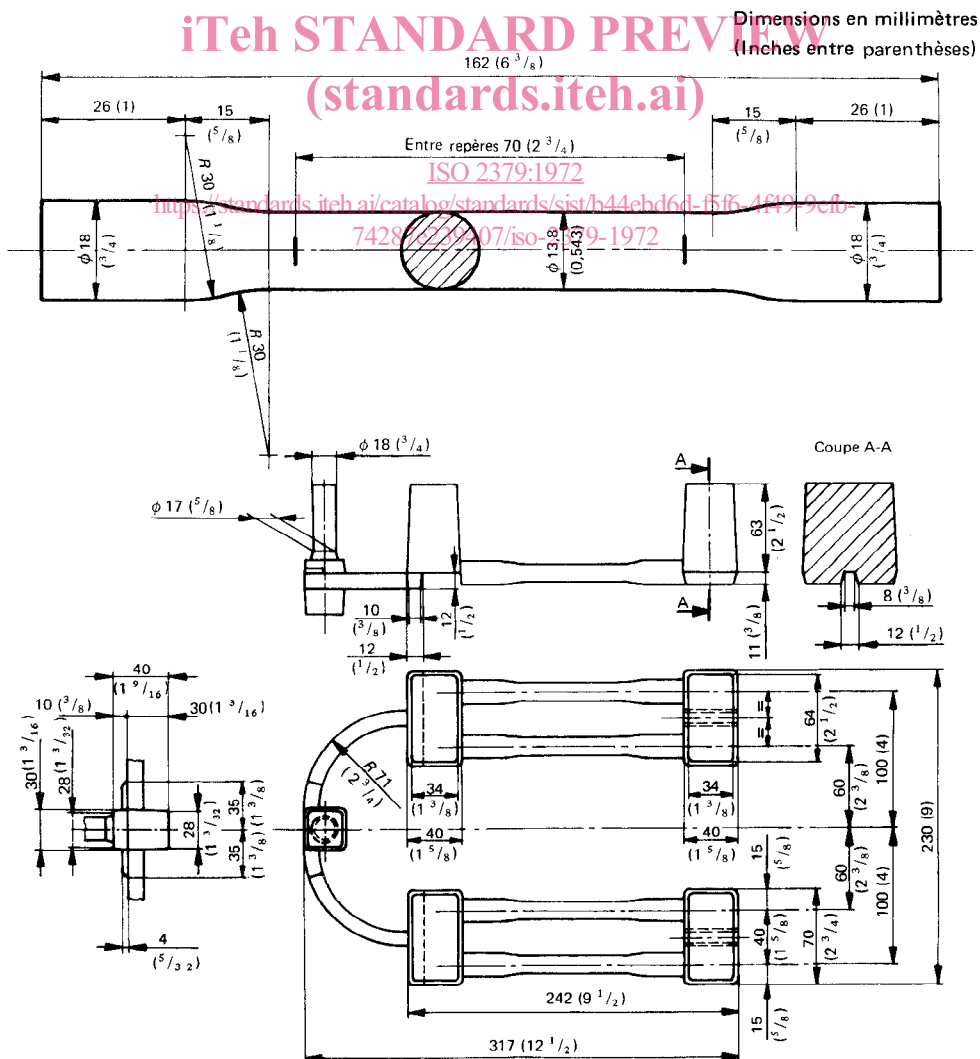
FIGURE — Éprouvette de référence et modèle de moule pour jeu de quatre éprouvettes
